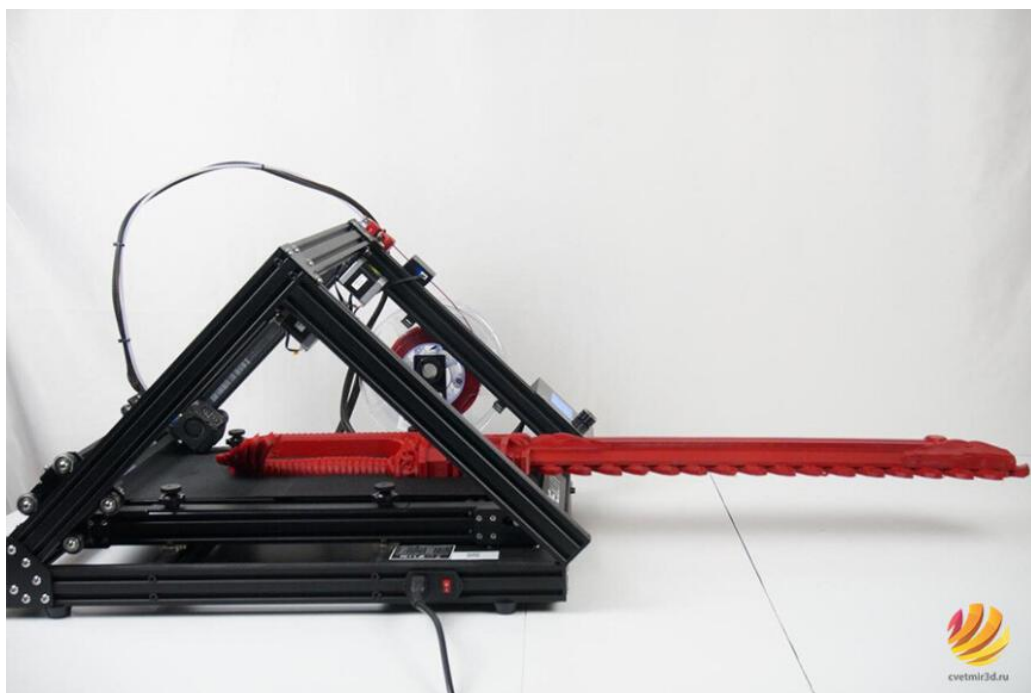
3D-принтер Crealty 3DPrintMill
